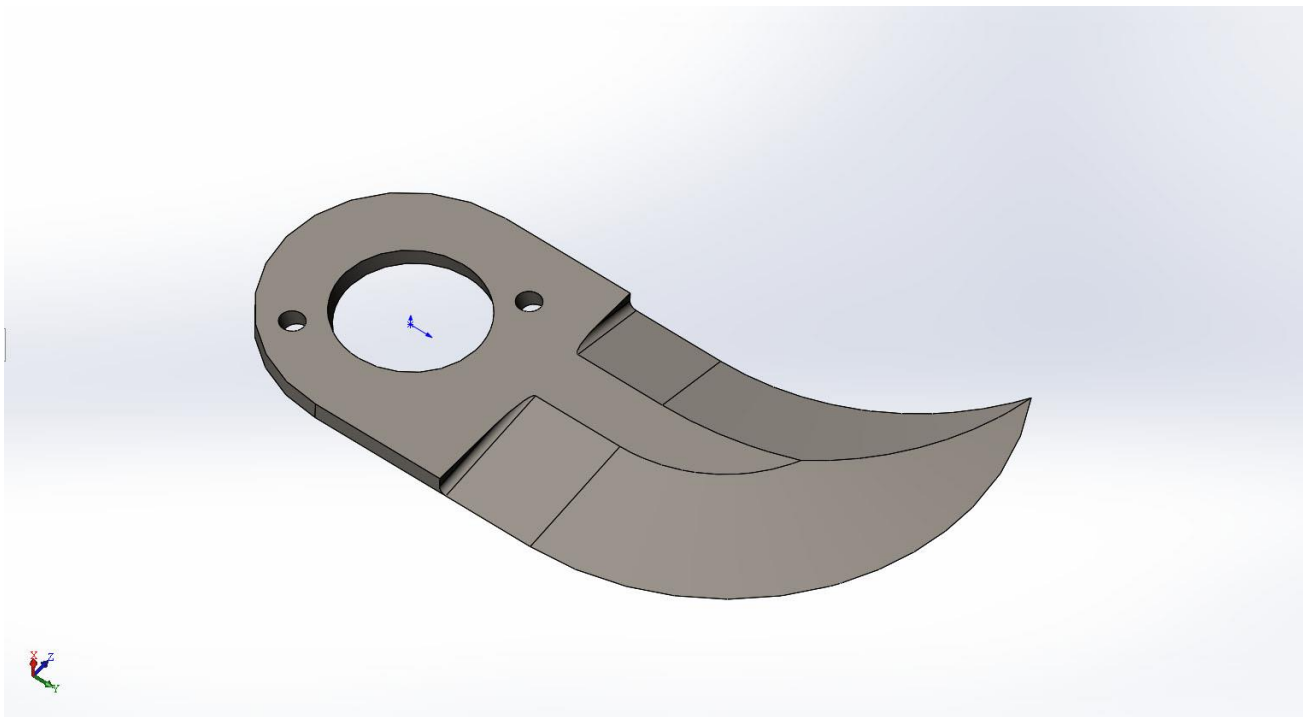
Базова конструкція ножа з двома сформованими кромками
